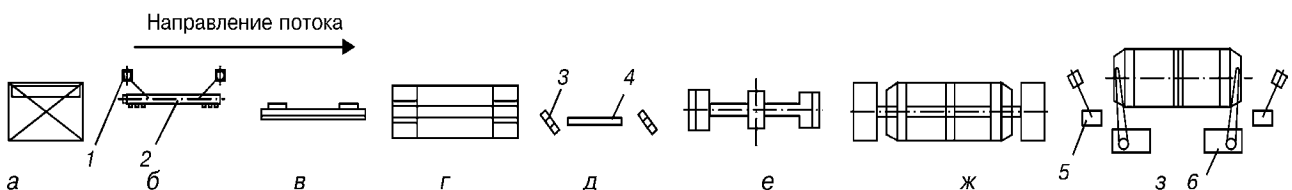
Схема участка сборки и сварки рам вагона-минераловоза: а — контейнер для зетового профиля; б — стэнд сборки хребтовой балки; в — установка автоматической сварки; г — двухсторонний сверлильный станок; д — тележка-кантователь для клепки упоров; е — стэнд сборки рамы; ж — цапфенный сварочный кантователь; з — стэнд сверловки и клепки пятников (остальные поз. см. в тексте)
